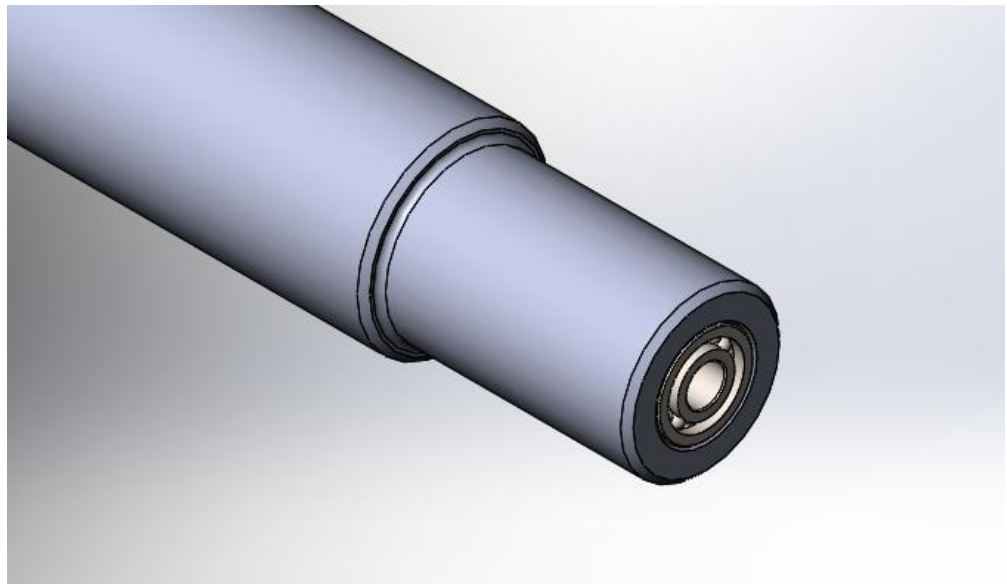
Підшипники на торцях валу барабана стрічкового дозатора модернізованої конструкції
